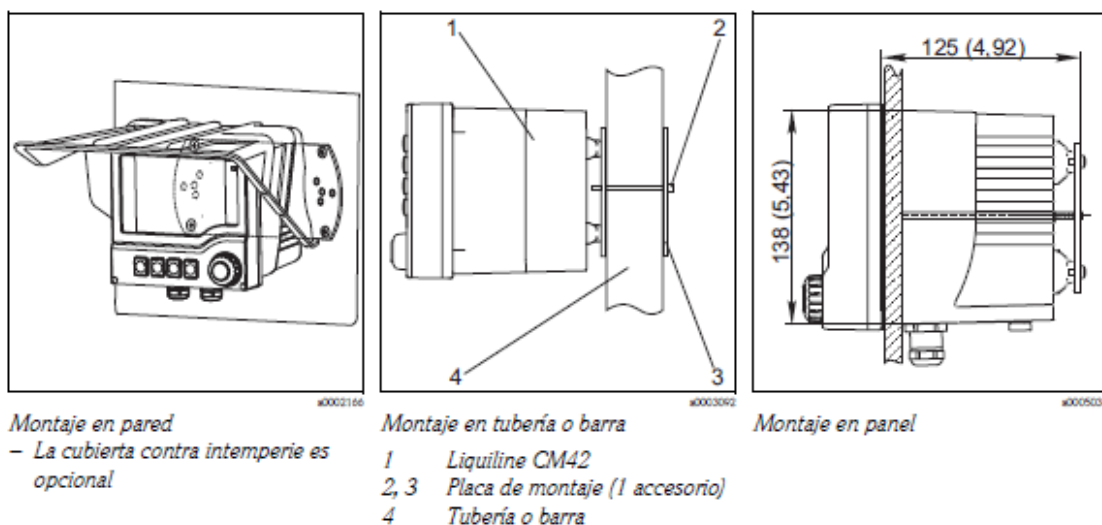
Por orden, montaje en pared, en tubería o en panel
